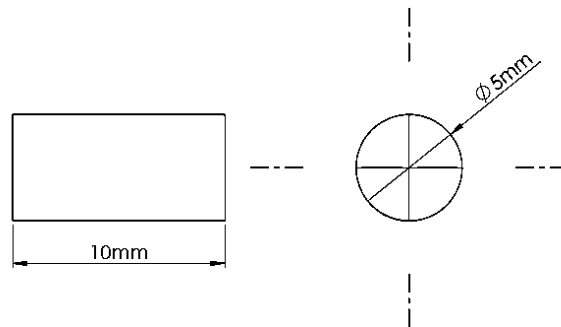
Dimensiones de la probeta de compresión en caliente de acuerdo con la norma ASTM E209.
